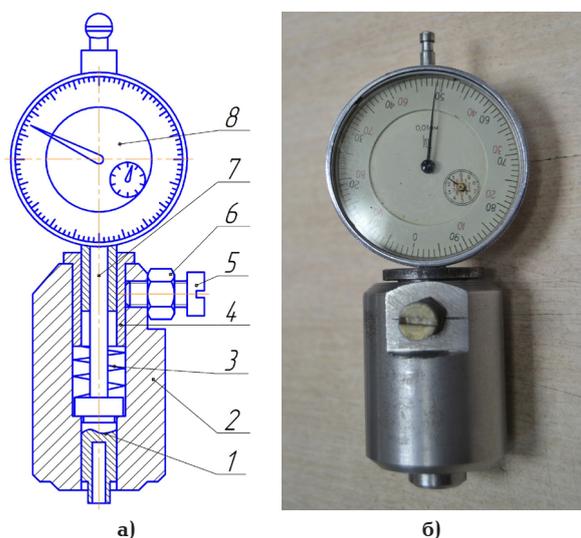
Разрез и общий вид универсального приспособления для определения хода иглы автомобильных (а)
